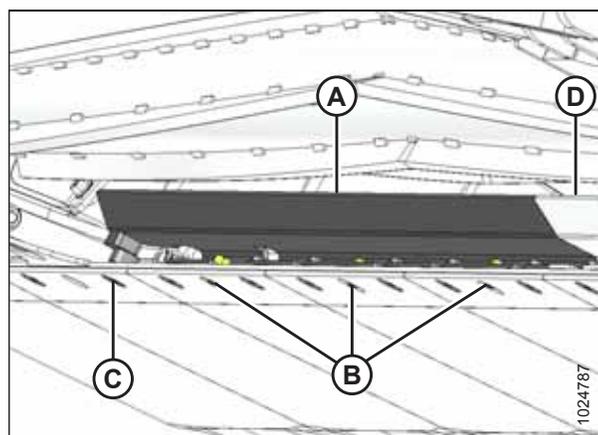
Déflecteur gauche de la barre de coupe vu du dessous de la barre de coupe
